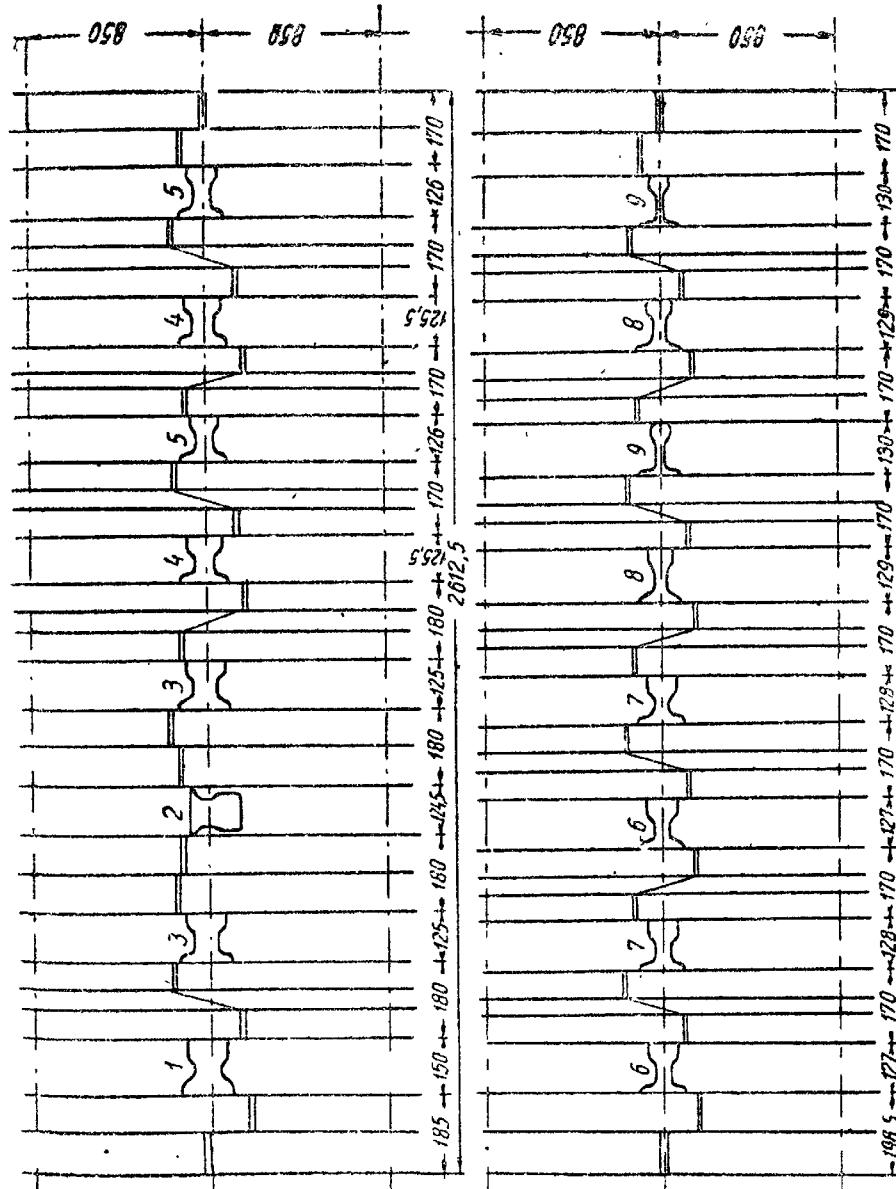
Калибровка рельса типа IIIA. Расположение ручьев в валках.
